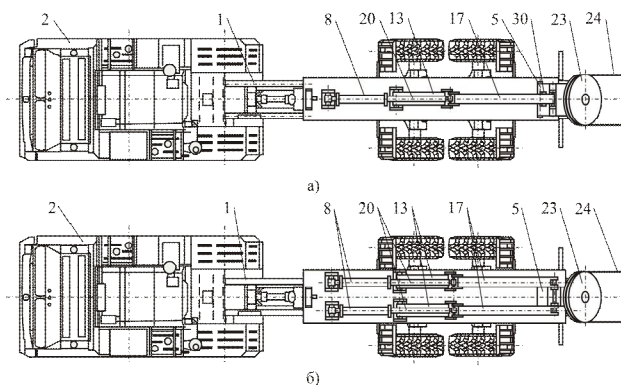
Общий вид самоходной машины (вид сверху) с выносным расположением концевой опоры и складывающейся штангой в рабочем положении в различных модификациях: а - с одинарной складывающейся штангой и одинарным гидроцилиндром (модификация Ву1-4/Х); б - с двумя складывающимися штангами и сдвоенными параллельно установленными и синхронно работающими гидроцилиндрами одинакового типоразмера (модификация Ву2-4/Х)
